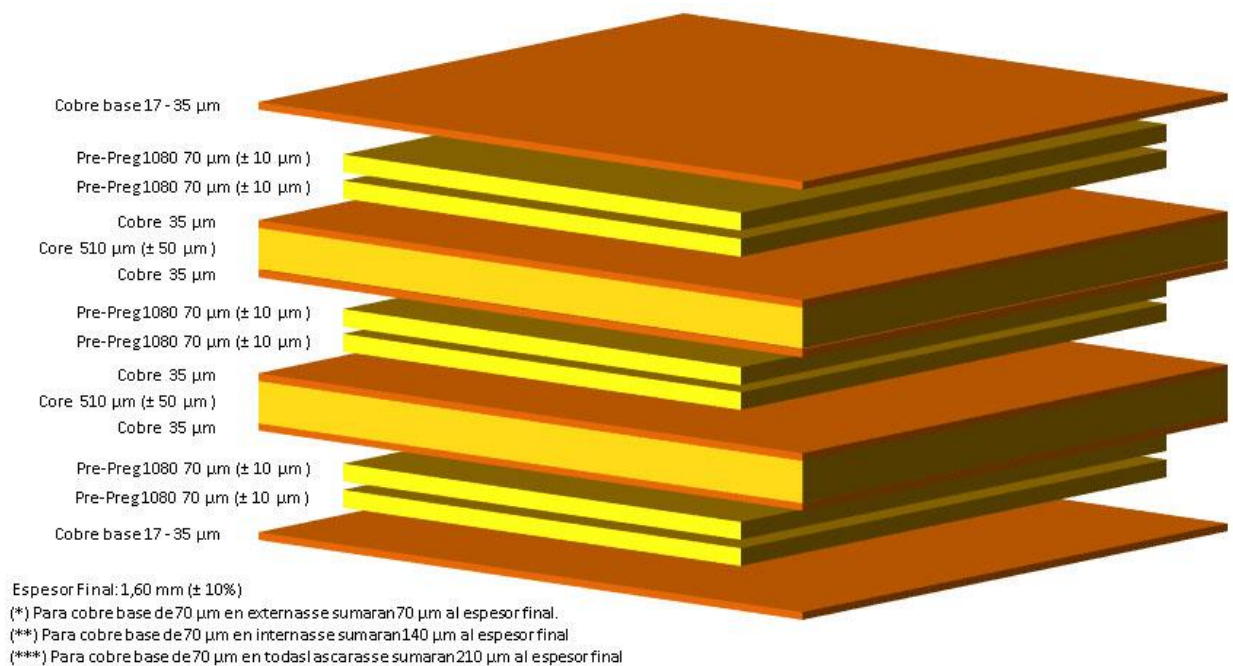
PCB de 6 capas 2 con doble cara. (Zubelzu, 2016)
